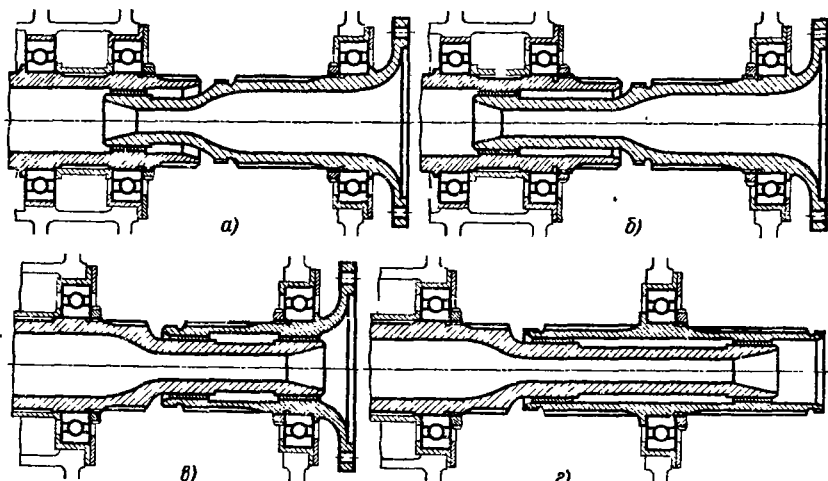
Совместная установка подшипников качения и скольжения в соосных валах
